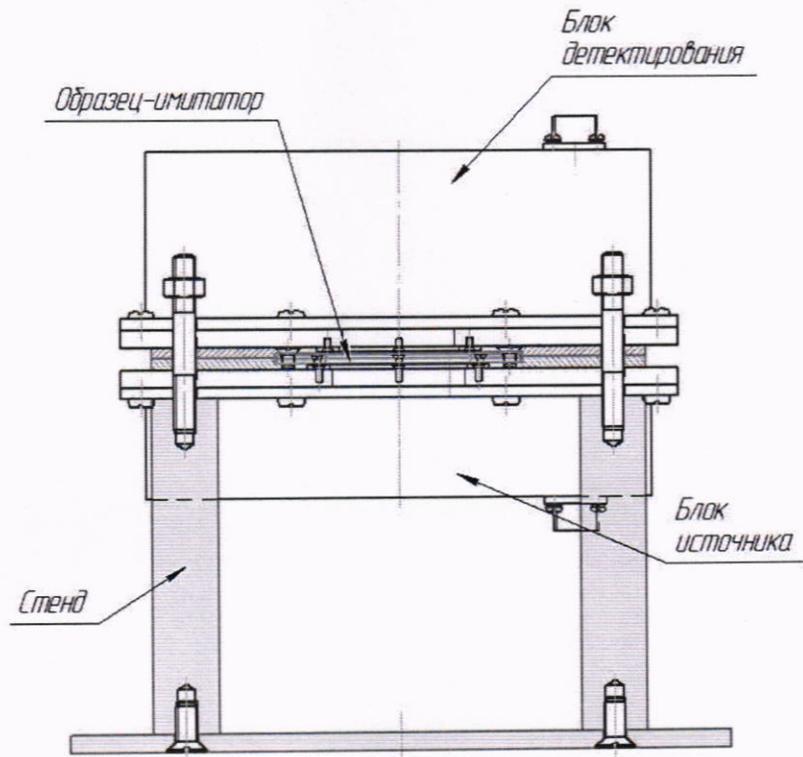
Установка толщиномера и образцов-имитаторов на стенде
